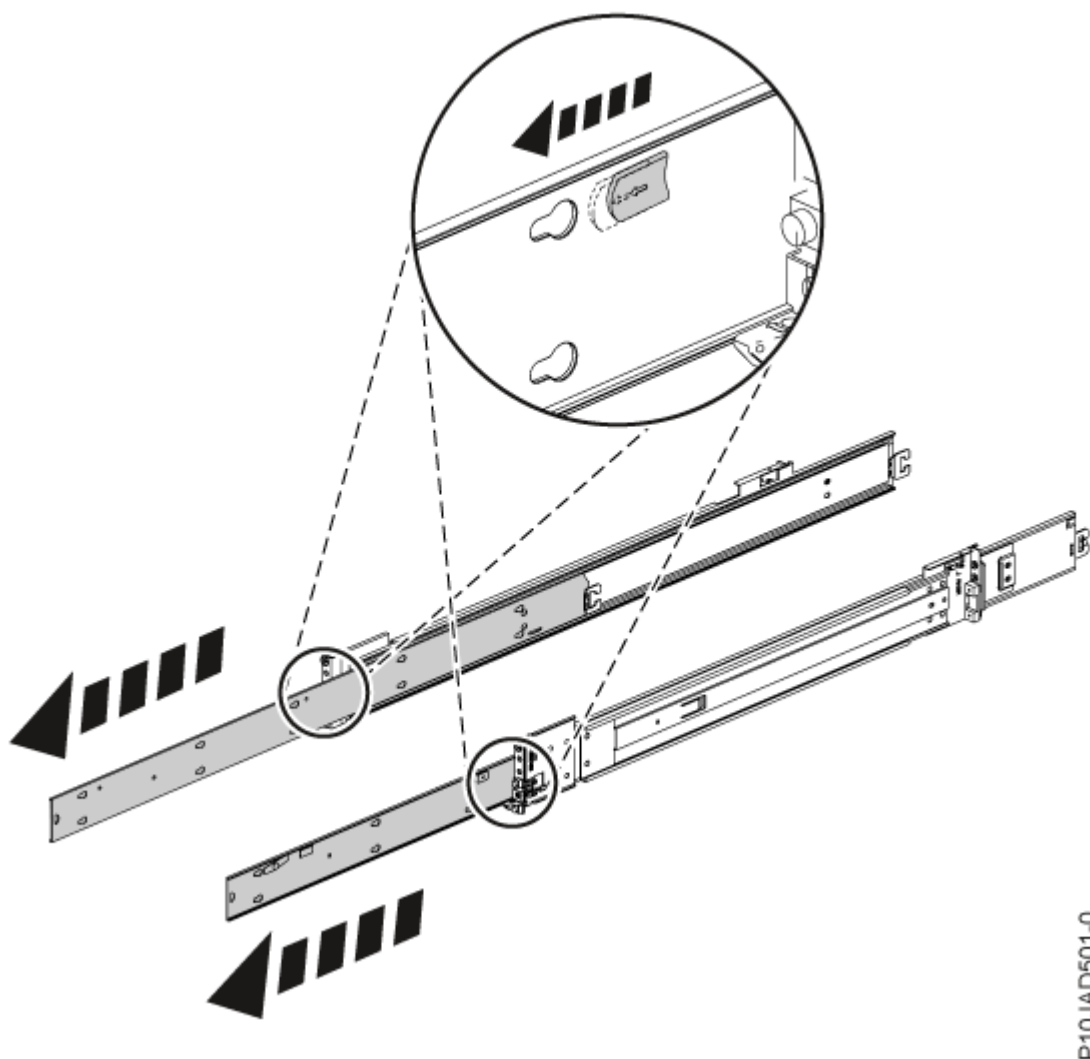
Appuyer sur la languette de verrouillage du rail intérieur
